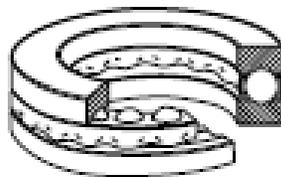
Rodamientos de bolas de apoyo axial de una sola dirección
